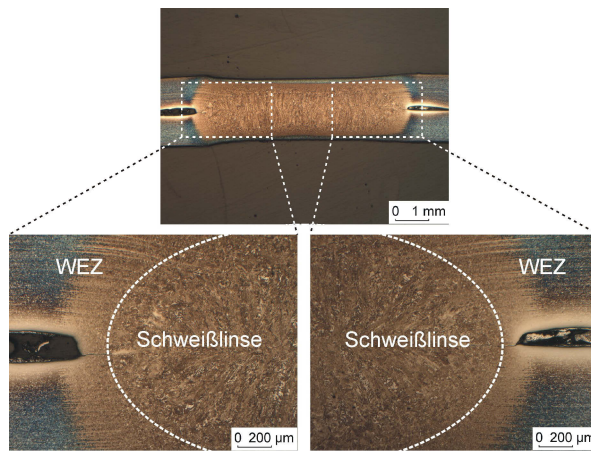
Metallografischer Schliff einer Punktschweißverbindung. (Material: HCT690T+Z140,  $t = 1 \text{ mm}$ ). Die Schweißlinse lässt sich anhand der Gefügeänderung sicher identifizieren. Direkt neben der Schweißlinse sind die Bleche durch den Anpressdruck noch nahezu formschlüssig verbunden, bei dem Spalt handelt es sich nicht um ein Fehlerbild (Quelle: BAM 5.5)
